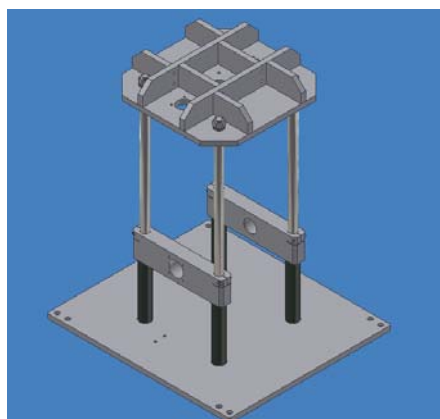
Estrutura, sub-conjunto N° 10300.
